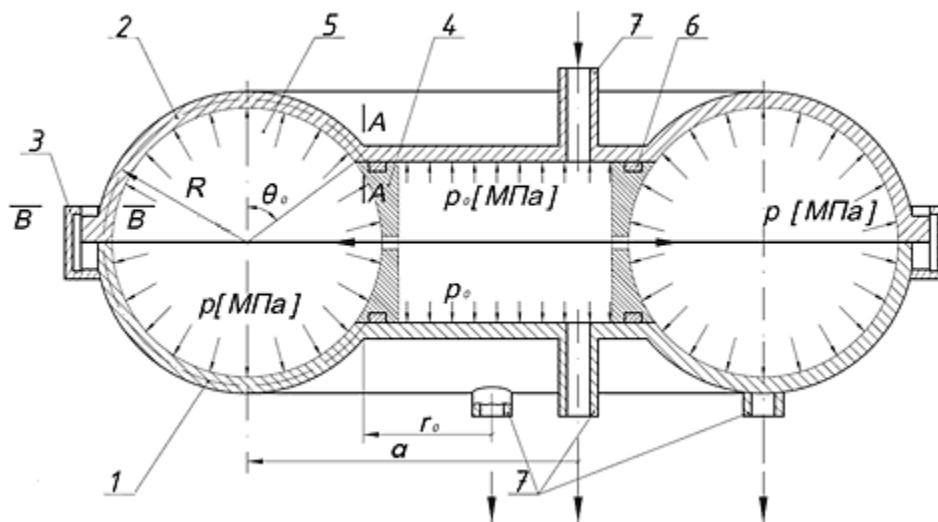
Конструкция баромембранного аппарата: 1 — крышка нижняя; 2 — крышка верхняя; 3 — кольцо замковое байонетное; 4 — плоскокамерный модуль; 5 — трубчатый модуль; 6 — уплотнение; 7 — входной и выходной патрубки
